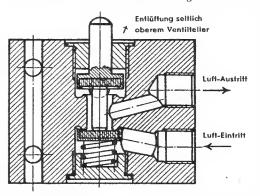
Steuer-Nockenventil, Grundtype 1 für Dreiwegesteuerung
